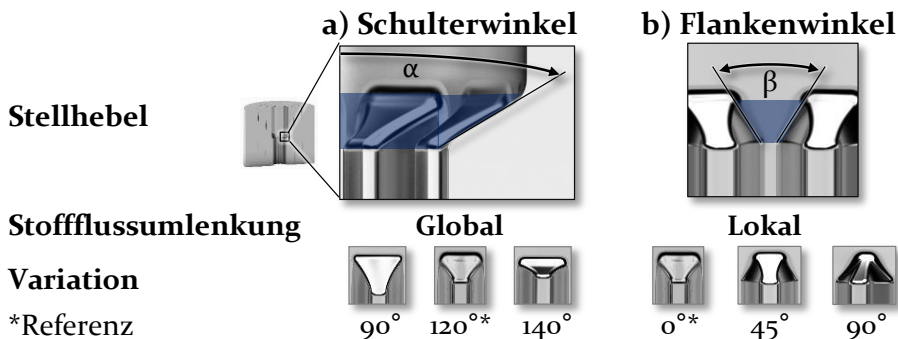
Untersuchte werkzeugseitige Stellhebel bei der Zahnradherstellung
